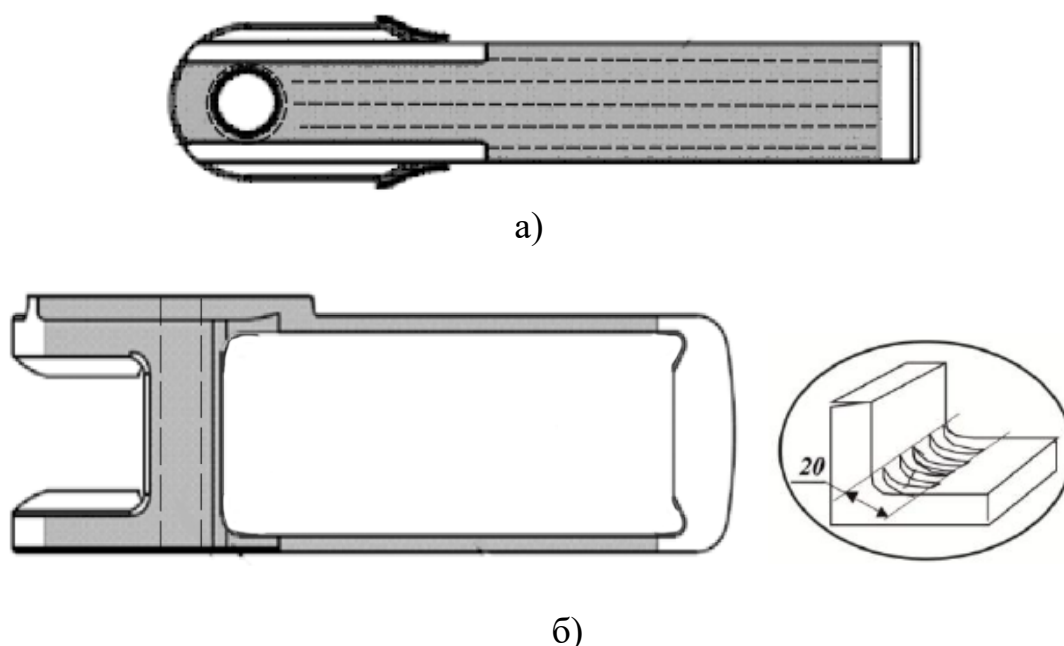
Схема сканирования корпуса тягового БСУ-ТМ136
